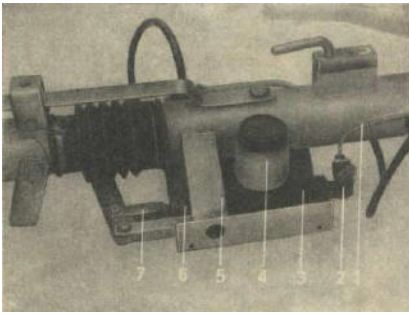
Hauptbremszylinder am Haltewinkel des Auflaufkopfes
